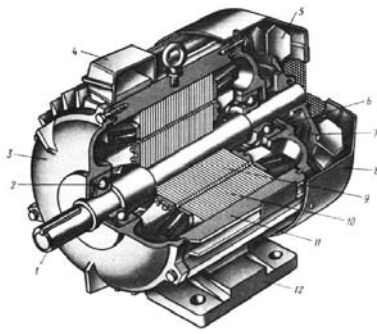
Конструктивная схема двигателя асинхронного типа ВАО2-315М4
